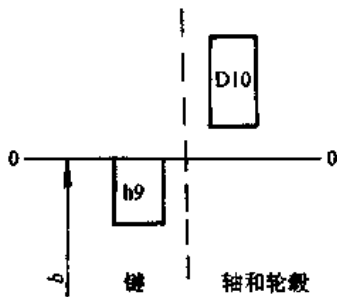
楔键配合尺寸 b 的公差带图
